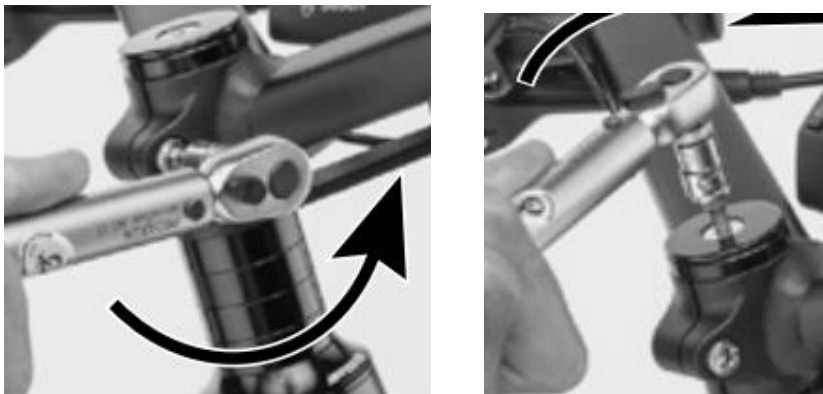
Première étape du serrage du jeu de direction : desserrer les vis de la tige F, puis serrer le capuchon supérieur.
